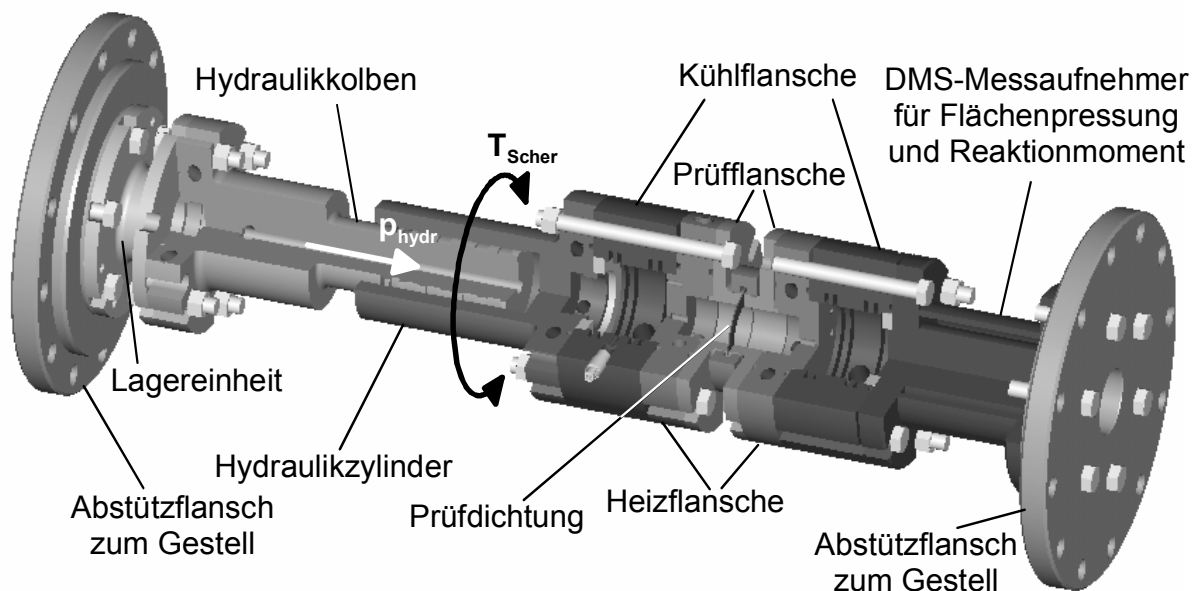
3D-Modellierung der Prü fzelle bestehend aus Hydraulikzylinder und -kolben, Kühl- und Heizflanschen sowie den beiden Prüfflanschen mit eingelegter Prüfdichtung
